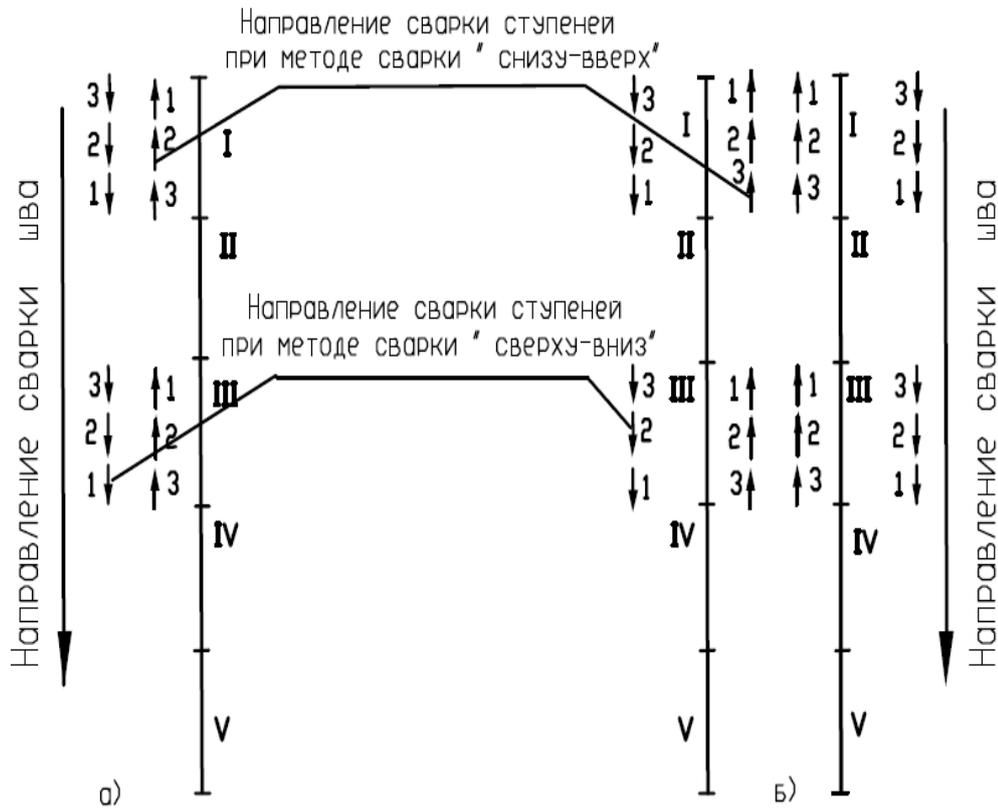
Последовательность сварки параллельных швов
